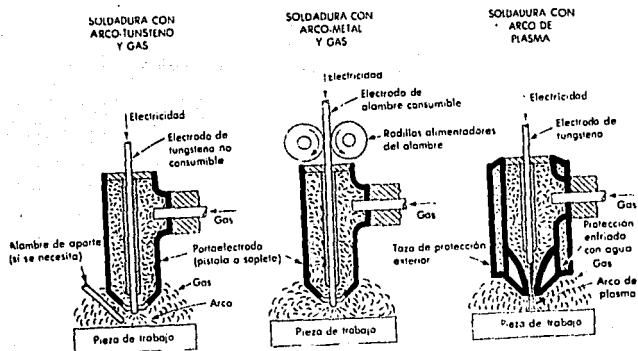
Soldadura con arco-tungsteno y gas.
